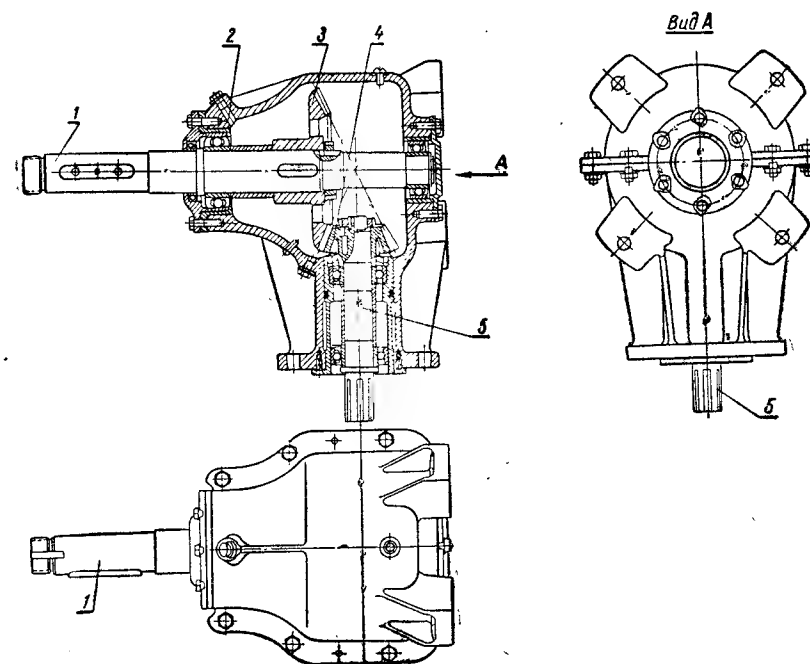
Верхний редуктор ветроагрегата «Бурянь» (2ВПЛ-4):
